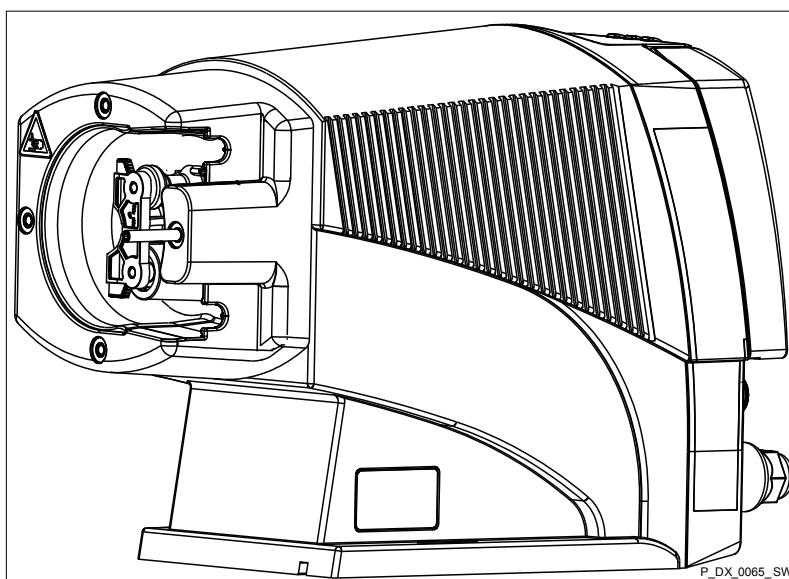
Estado inicial del rotor (tapa de cojinete oculta)
